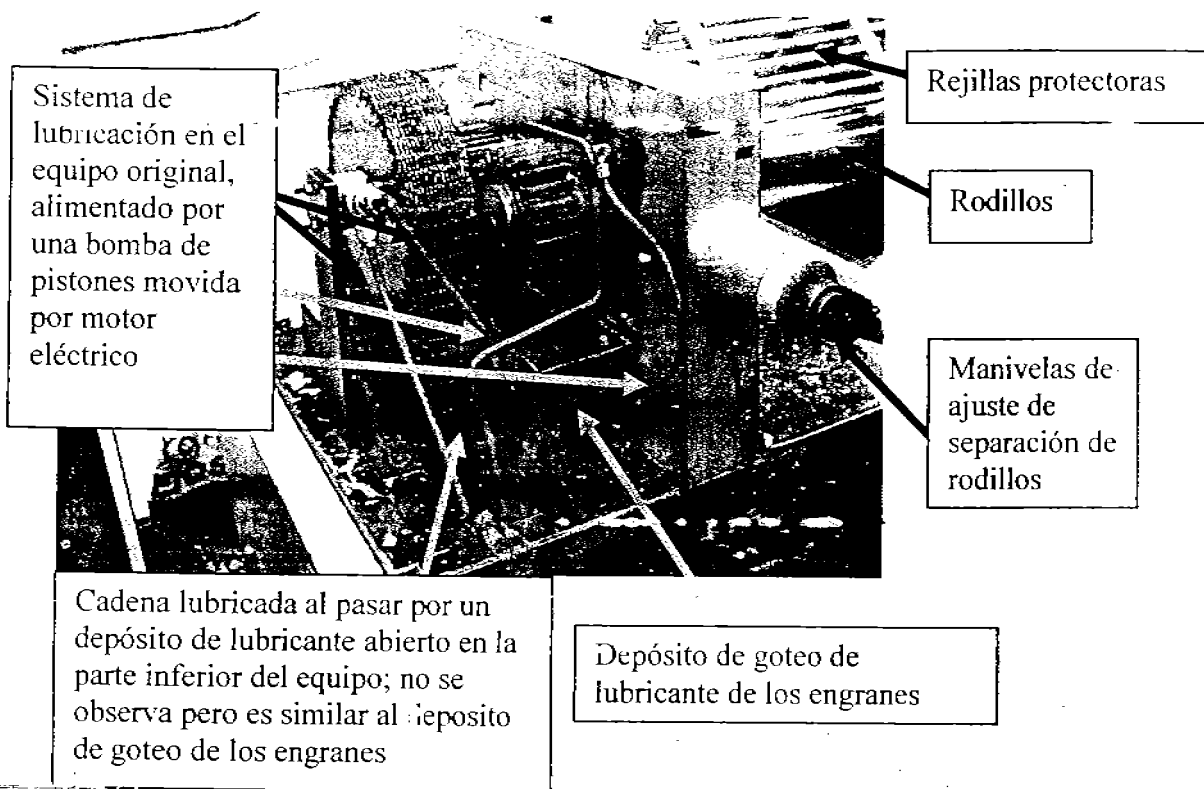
Lubricación en cadena, engranes y rodamientos de rodillos
